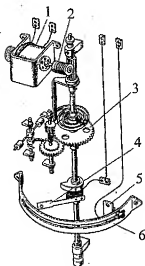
Конструкция реле времени с соленоидным приводом: 1 — соленоид; 2 — червячная передача; 3 — часовой механизм; 4 — подвижный контакт; 5 — неподвижный контакт; 6 — шкала выдержек времени
